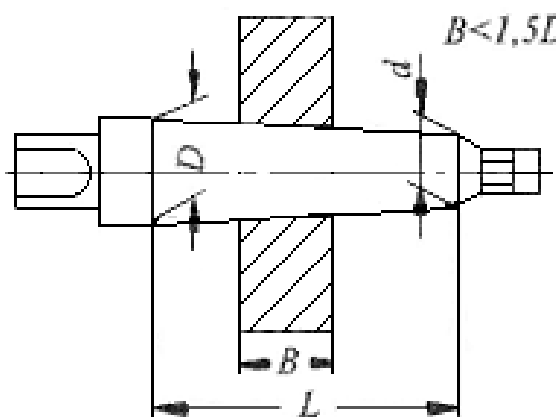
Установка заготовок на жорсткій конічній оправці
